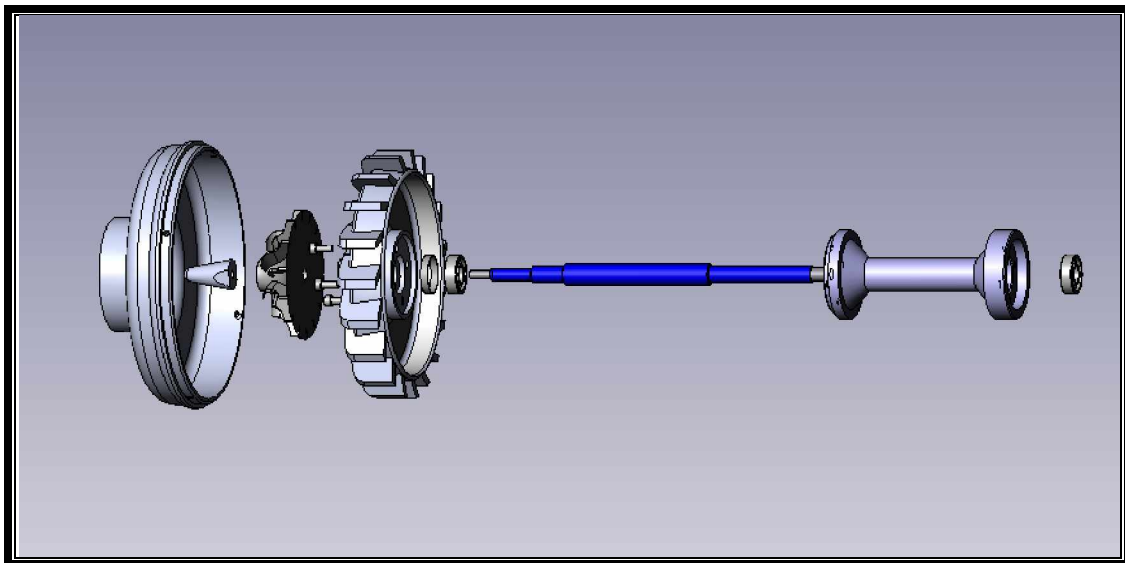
Vue d'ensemble des pièces réalisées.
